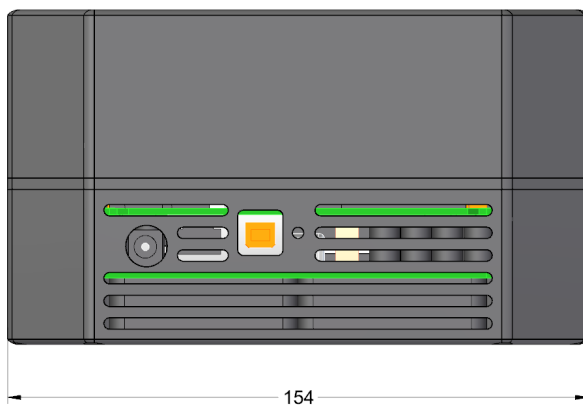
Boční pohled na hlavu kamery G3 se standardním chlazením a interním filtrovým kolem
